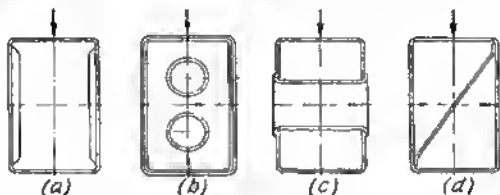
Vigas de paredes delgadas de sección rectangular con riostras transversales
